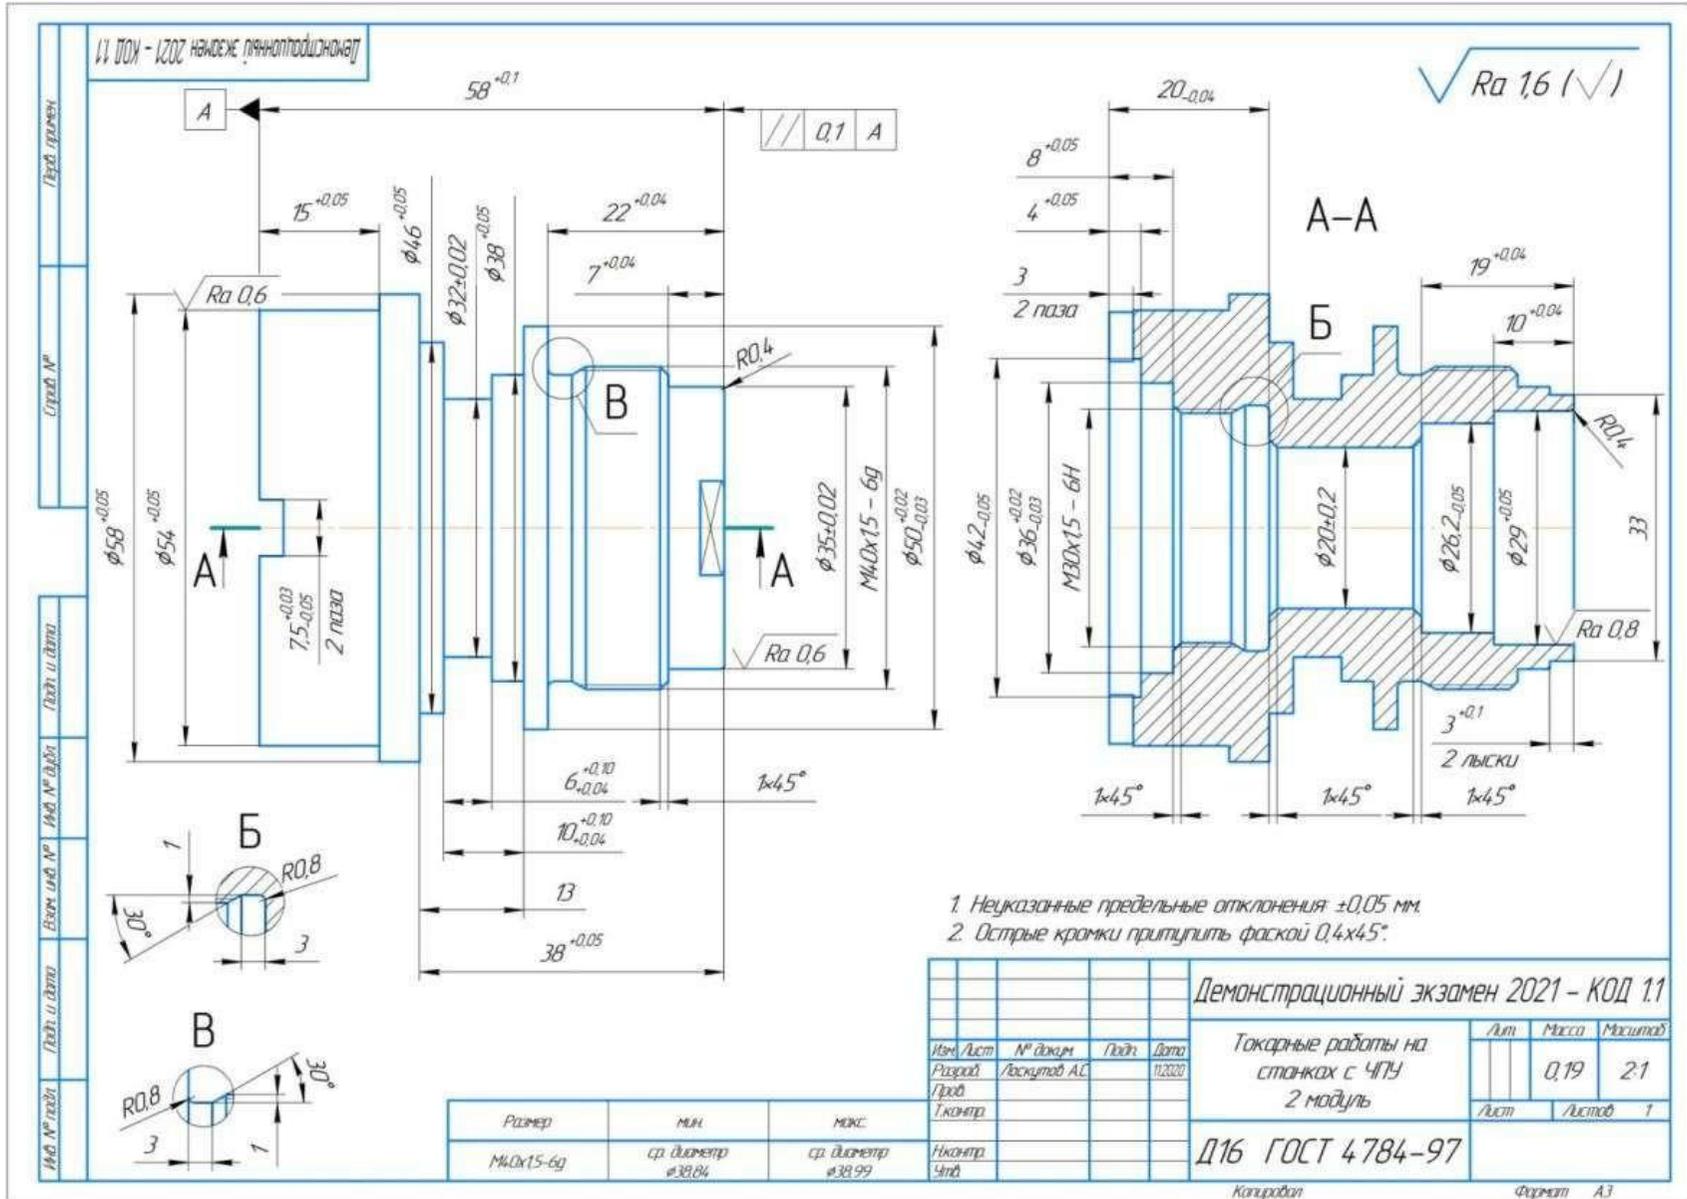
Чертеж детали Токарной работы на станках ЧПУ 54
